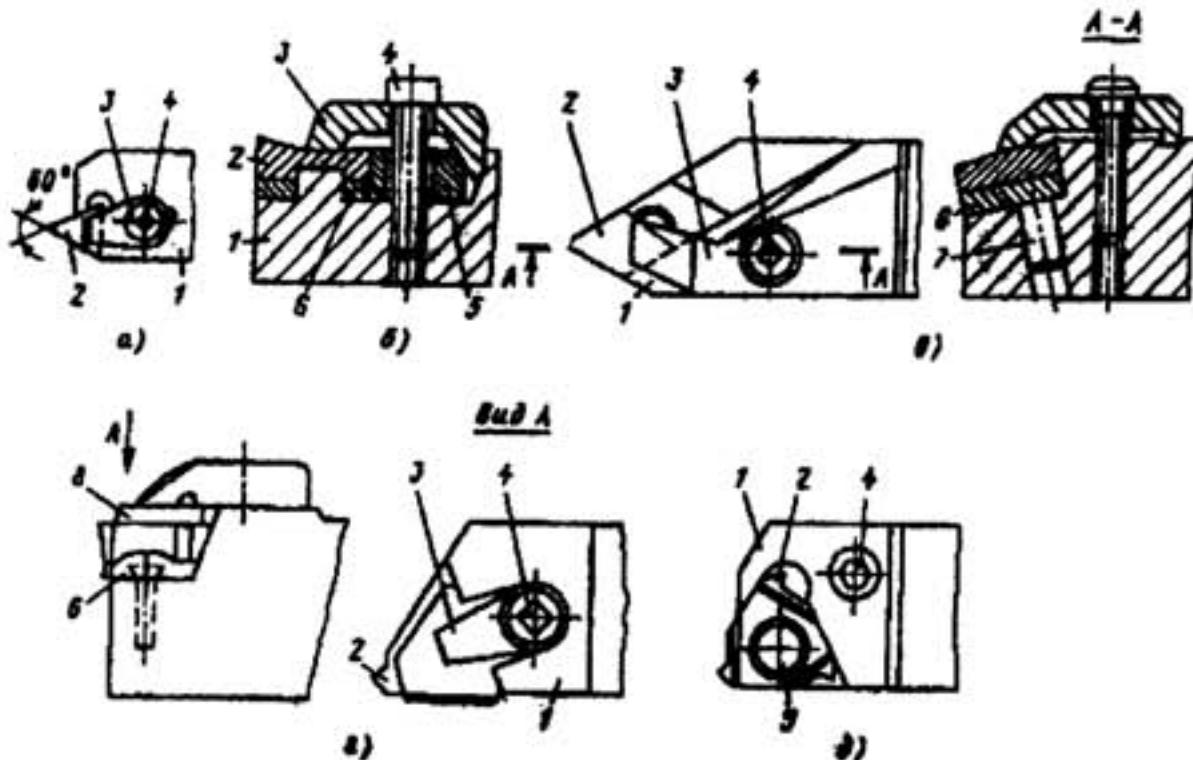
Конструкции резьбовых резцов с многогранными пластинами:
